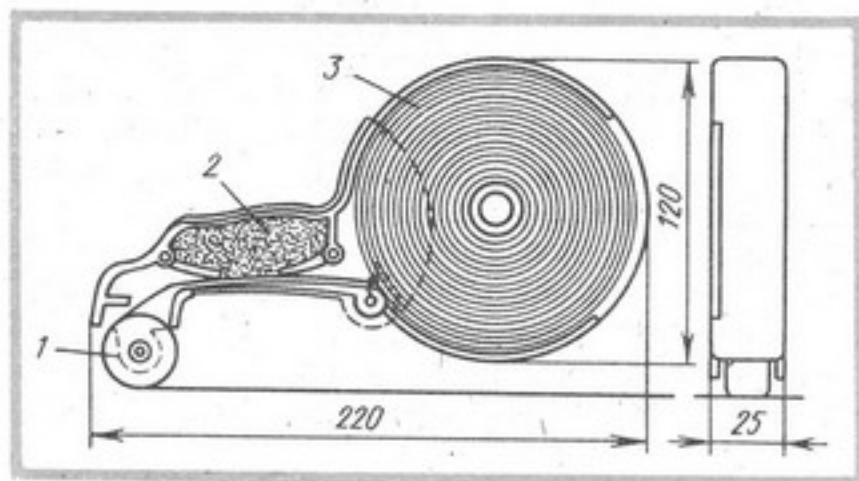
Приспособление для стяжки шпона клеевой лентой:
